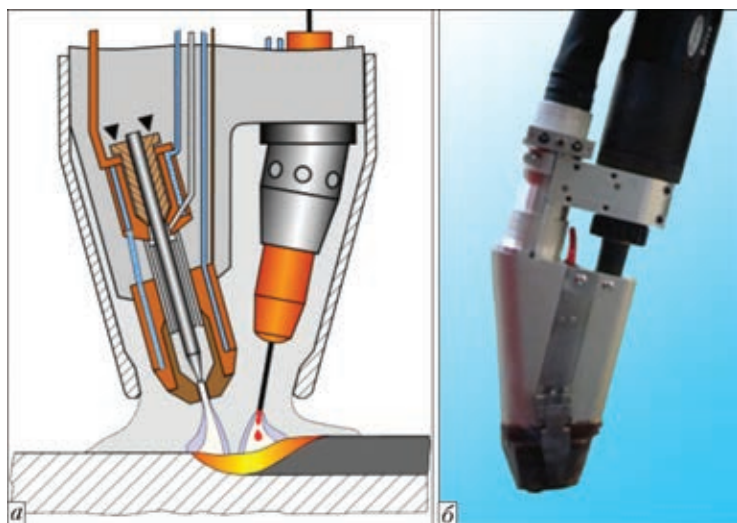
Схема процесса (а) и сварочная горелка для процесса Super-MIG (б)
